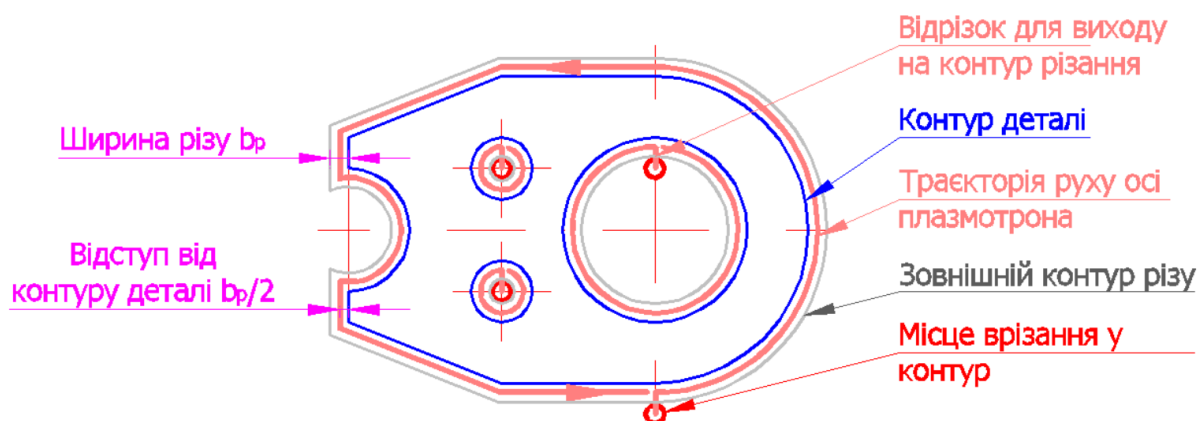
Схема утворення контуру деталі під час повітряно-плазмового різання
